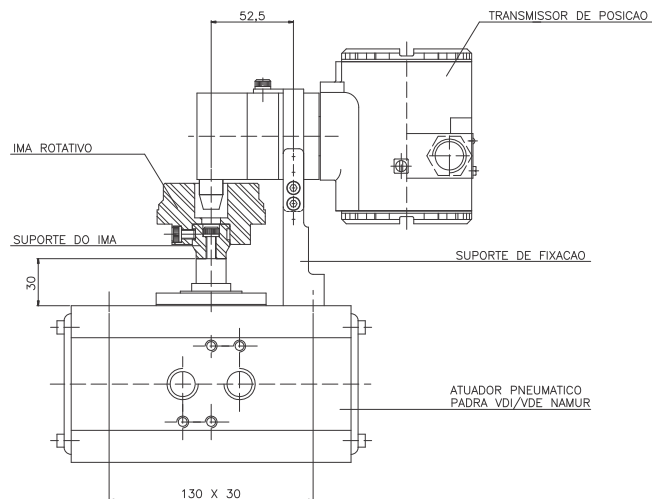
b – Desenho Dimensional do Sensor Remoto
